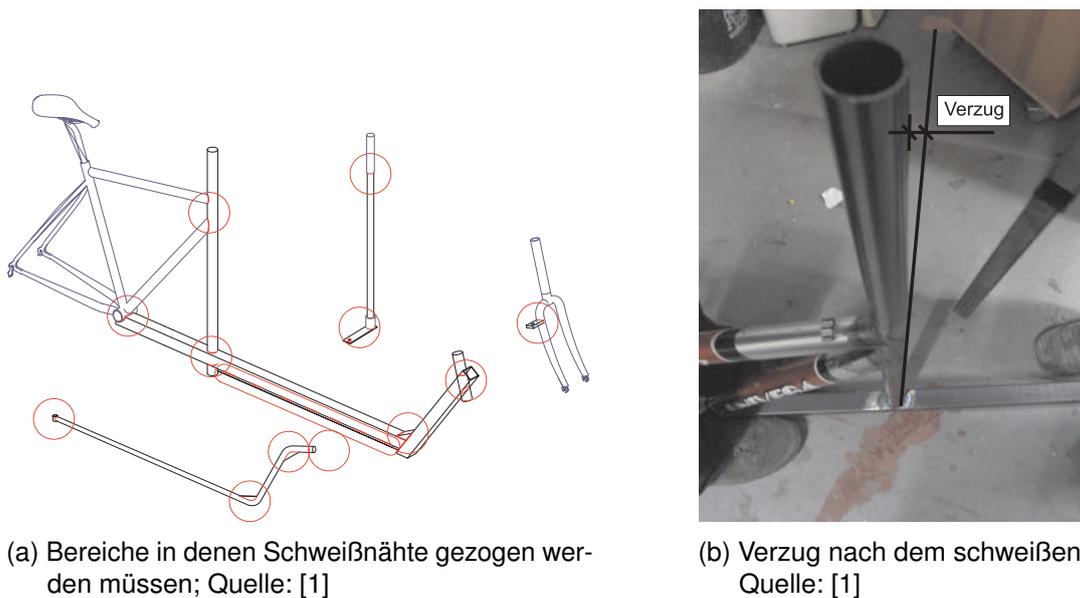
Endgültiges setzen der Schweißnähte sowie das Ausrichten nach dem schweißen
